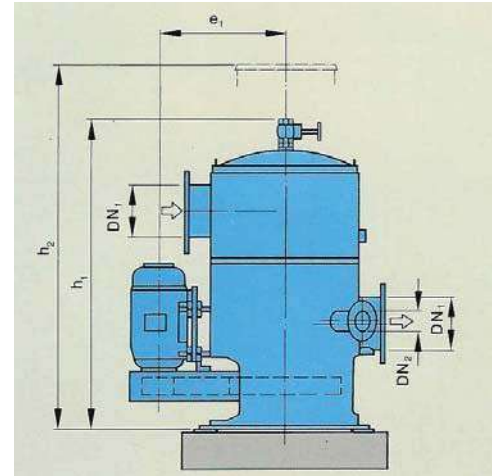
Dimensiones del depurador vertical, tamaño 10 ó 12.
